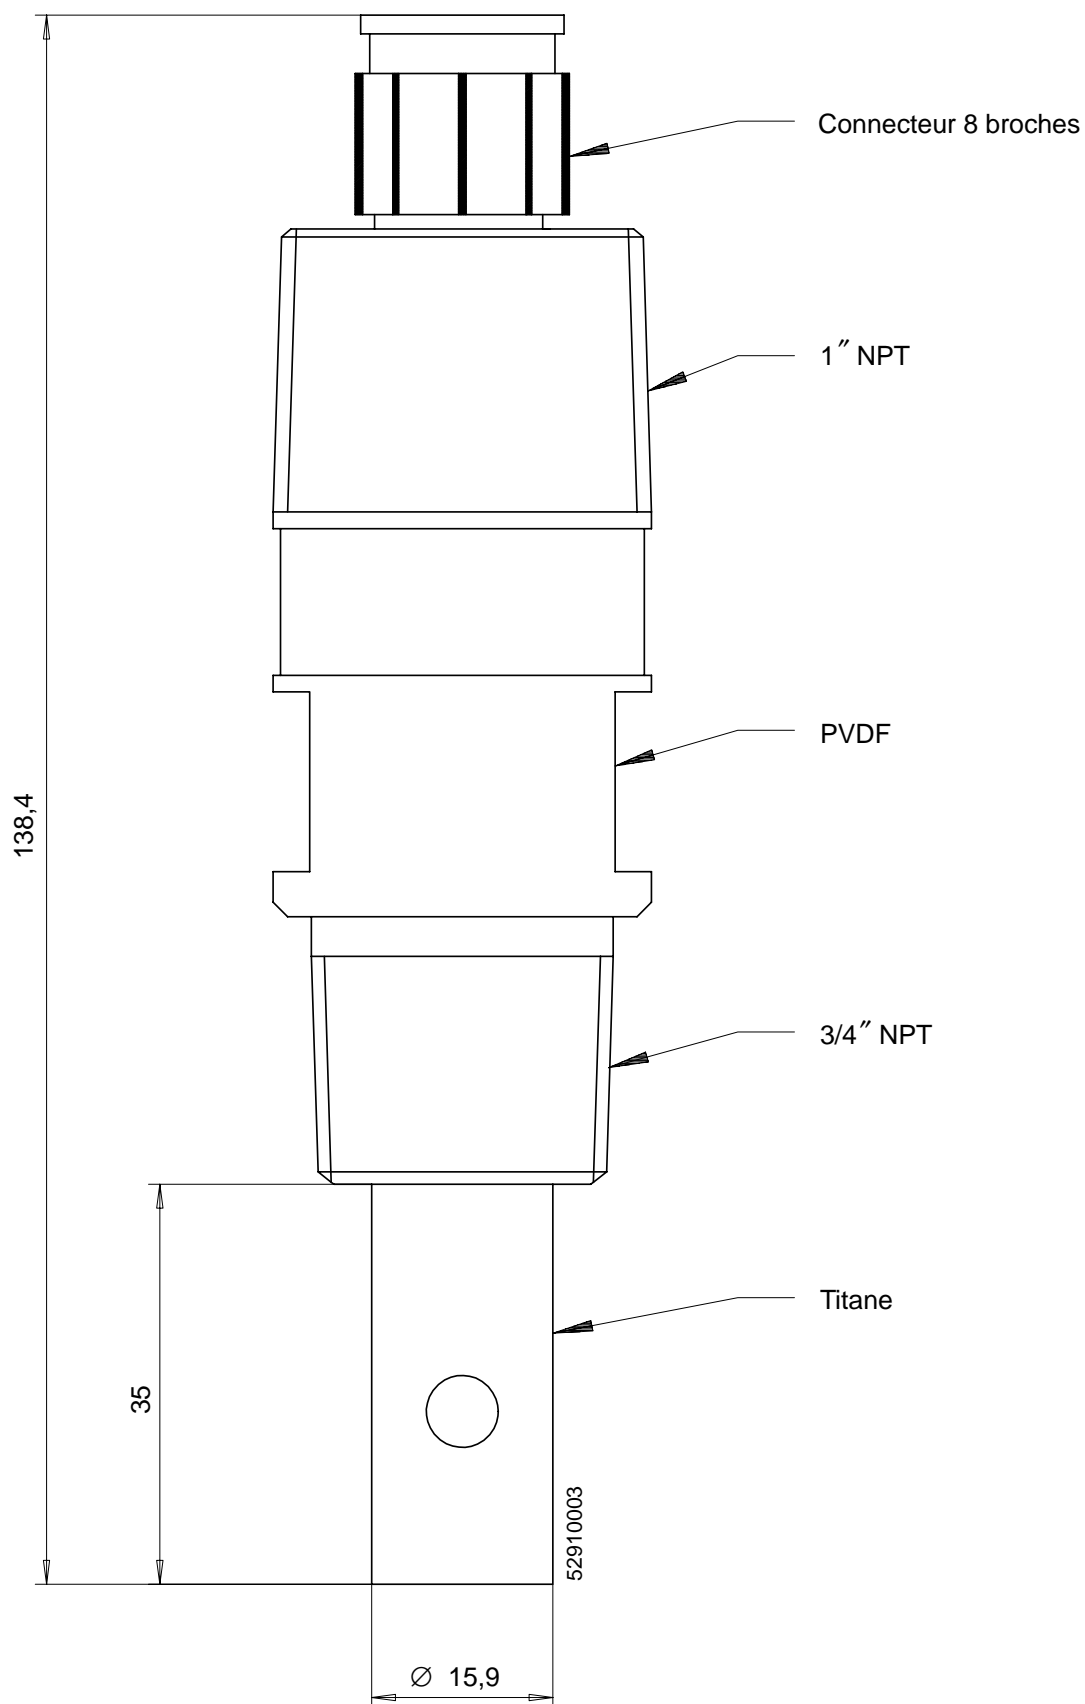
Dessin d'encombrement InPro[®] 7000
